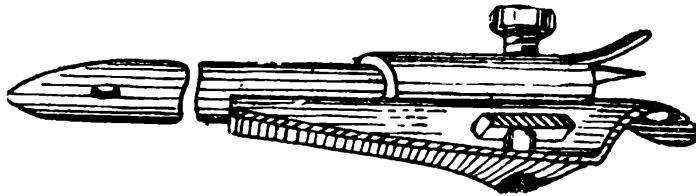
Инструмент для образования торцевой порезки в резиновой подошве
